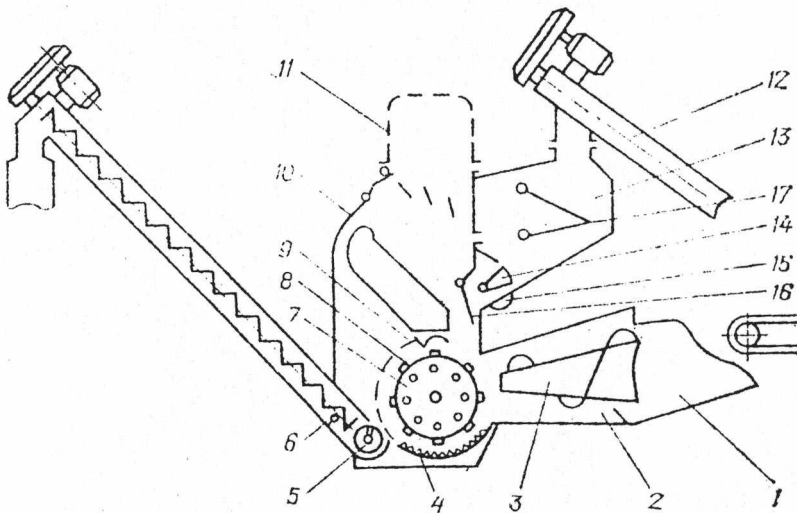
Структурна схема дробарки ДКМ-5: 1 - лотік; 2 - зовнішній шнек живильника; 3 - внутрішній шнек; 4 - дека; 5 - шнек дробарки; 6 - розвантажувальний шнек; 7 - молотковий ротор; 8 - камера подрібнювання; 9 - решето; 10 - пиловідокремлювач; 11 - фільтр; 12 -завантажувальний шнек; 13 - бункер, 14 - заслінка; 15 - магнітний сепаратор; 16 - заслінка; 17 - датчики рівня.
